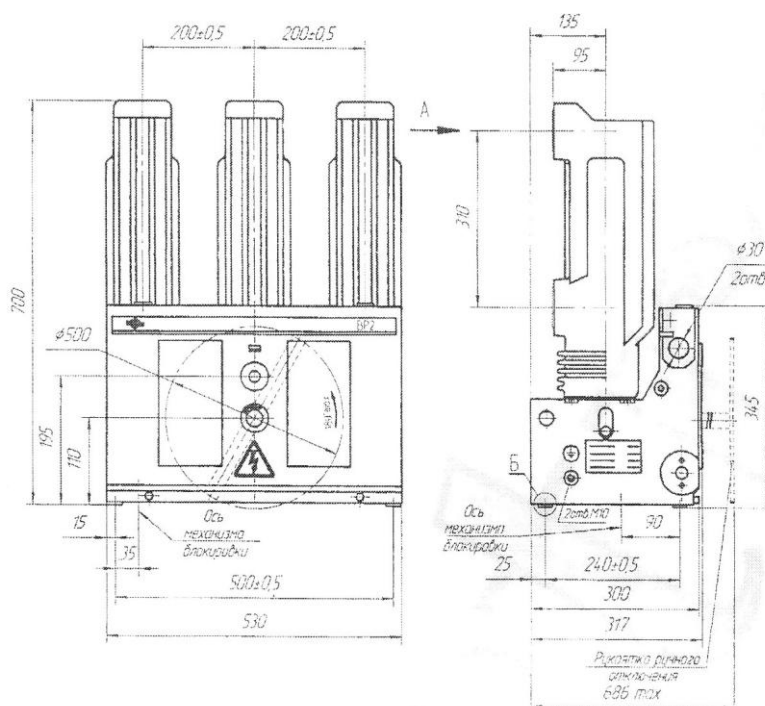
Внешний вид и габаритные размеры выключателя ВР2-10-31,5/2000 У2
